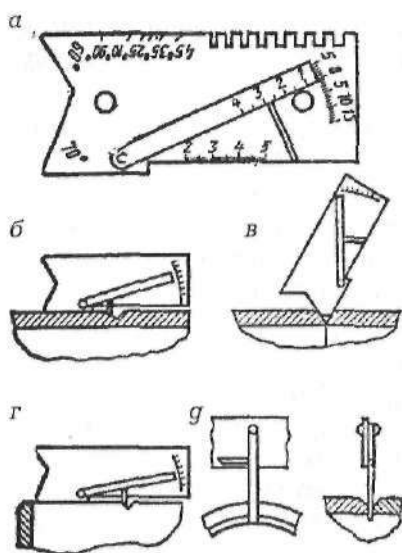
Универсальный шаблон сварщика (а) и примеры его использования для контроля глубины раковин (б), забоин (в), формы разделки стыков (г), ширины зазора (д)
